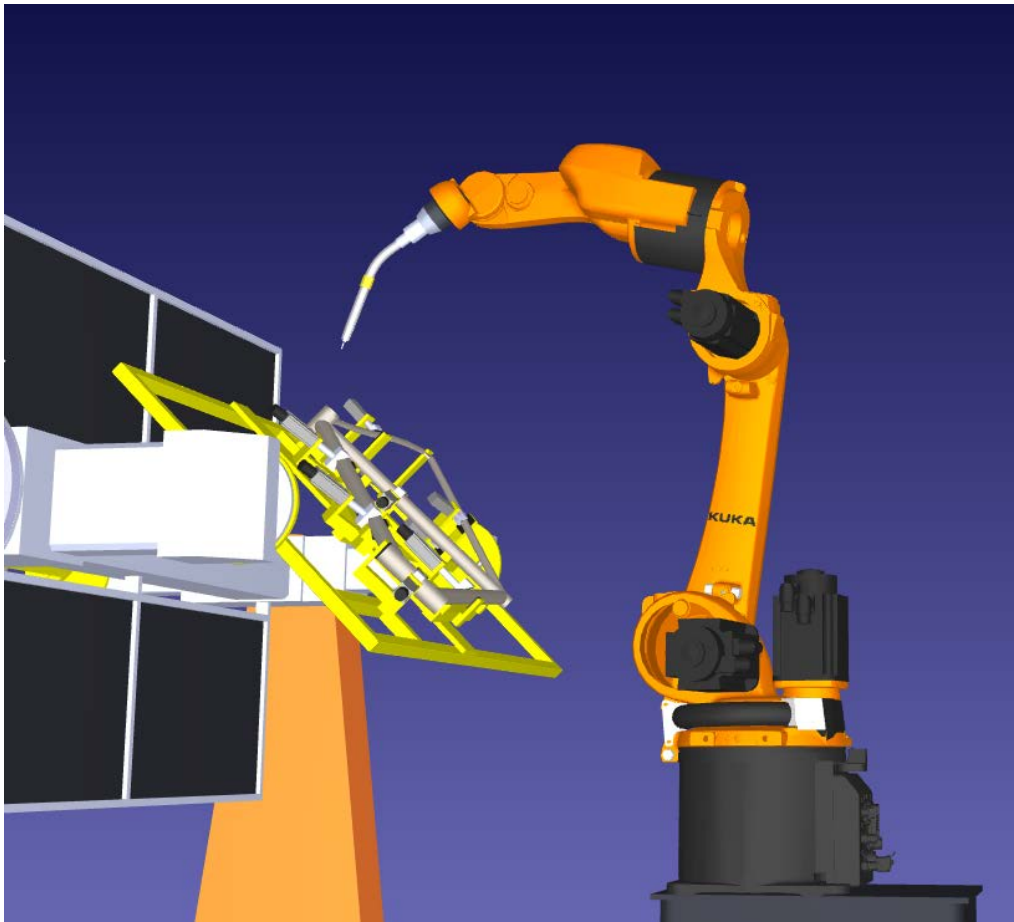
Стартова точка роботи зварювального робота KUKA KR 16 R1610
